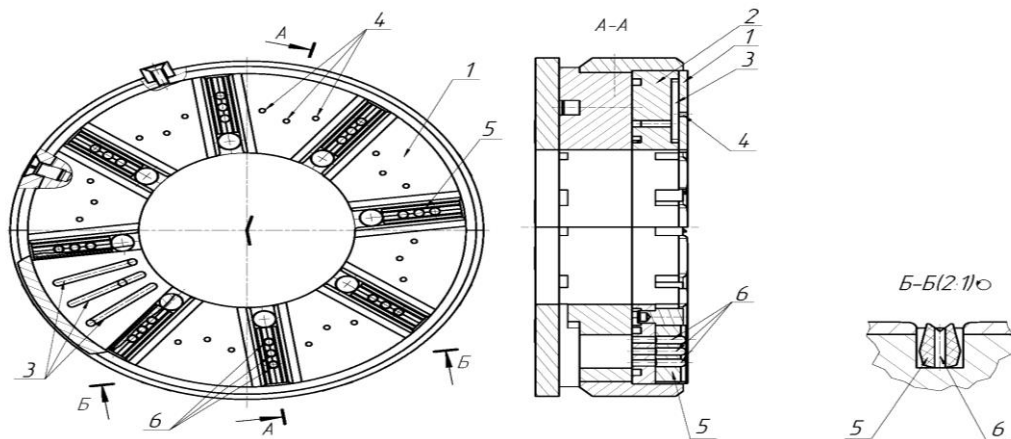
Реверсивний упорний підшипник з нереверсивними властивостями
